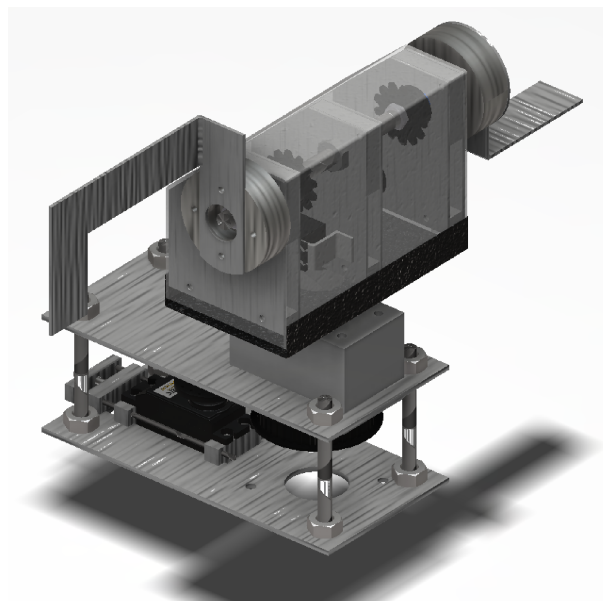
3D-Konstruktionsplan Antennennachführung
